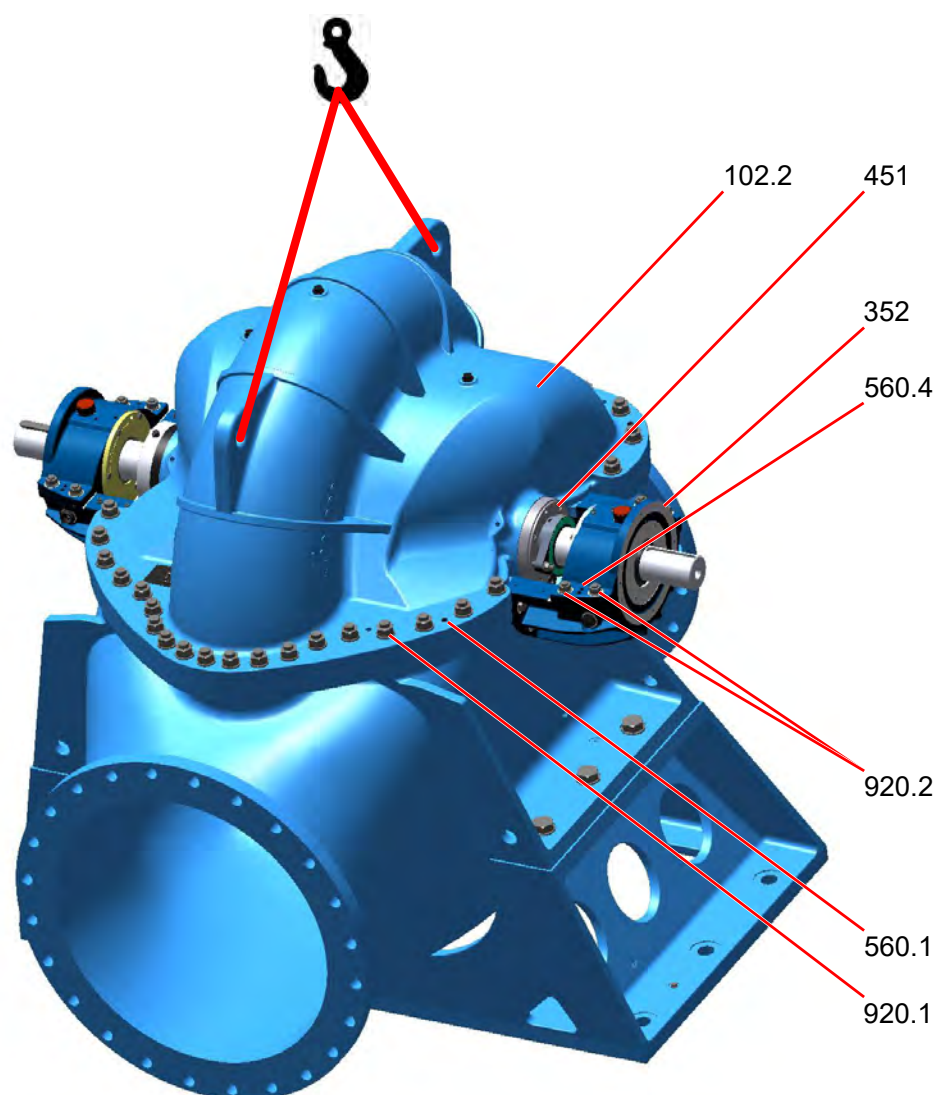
Демонтаж верхней части корпуса — ASP с платформой
